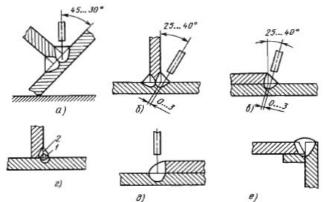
Схемы сварки угловых швов: 1 и 2 - первый и второй проходы[8].
